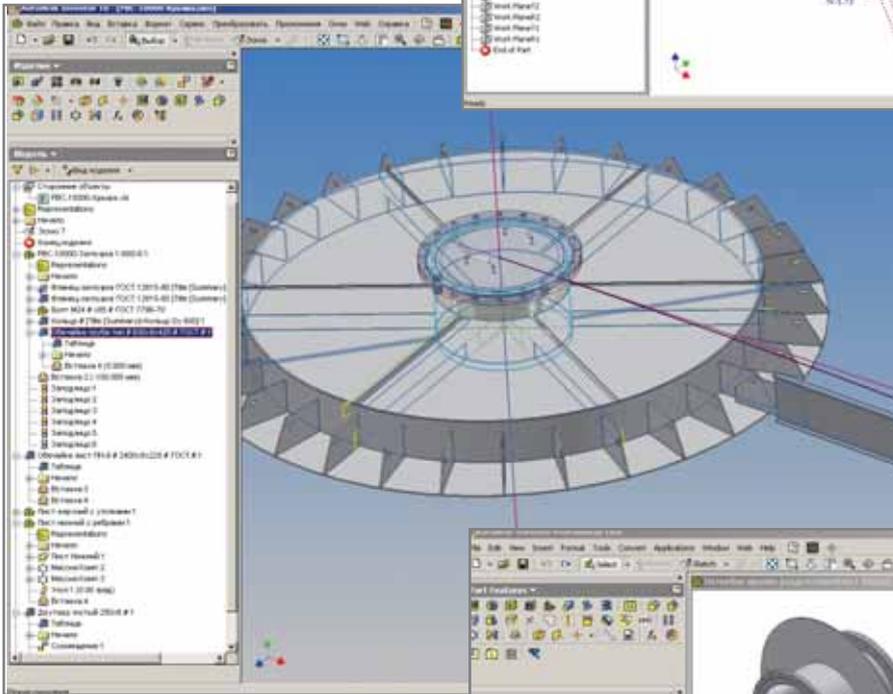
Модель сборки укрупненных щитов сферической крыши резервуара
